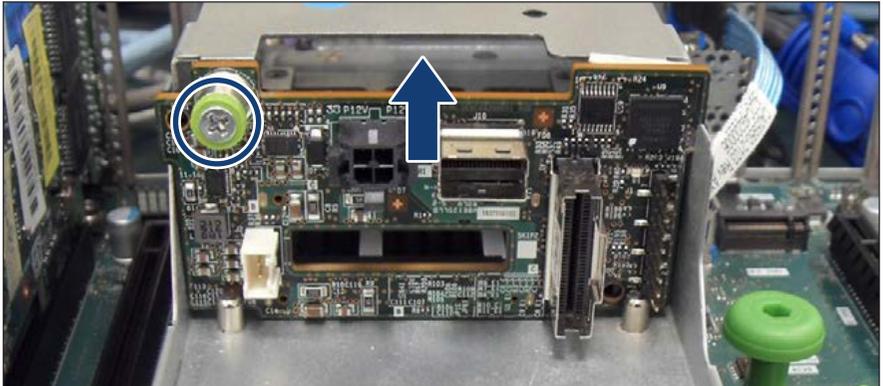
Rückseitige 2x 2,5-Zoll-HDD-Backplane entfernen
